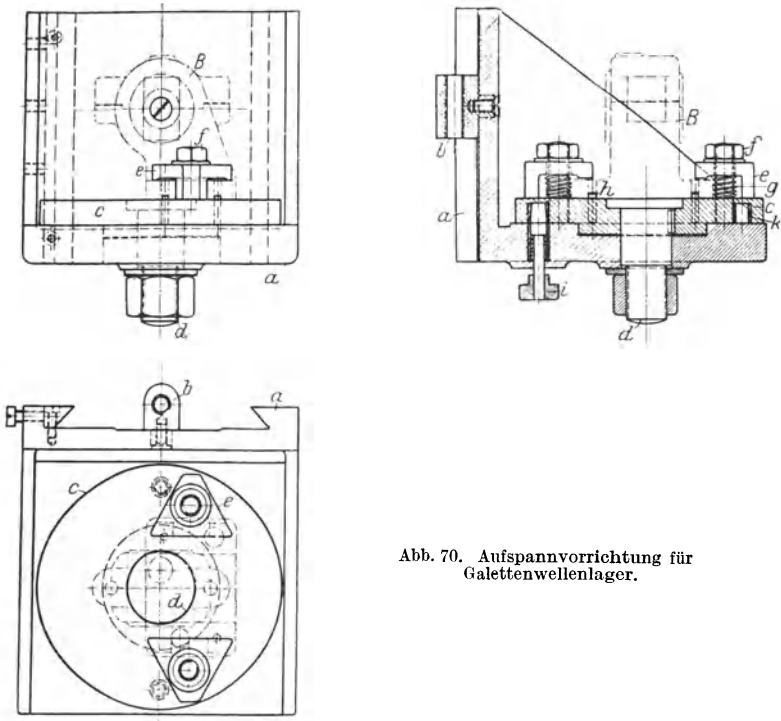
Aufspannvorrichtung für Galettenwellenlager.
